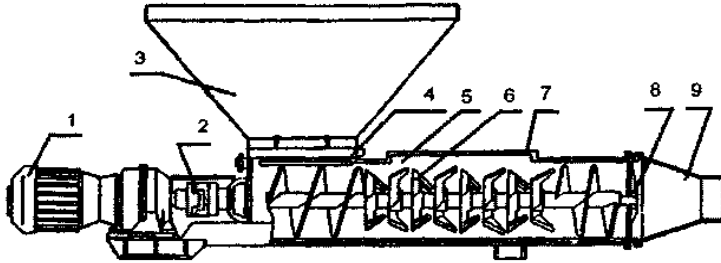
Кормозмішувач 40А: 1 - електродвигун; 2 - муфта; 3 - завантажувальний бункер; 4 - пристрій для подачі води; 5 - робоча камера; 6 - місильні лопаті; 7 - оглядовий люк; 8 - розвантажувальне вікно; 9 - конічна насадка
